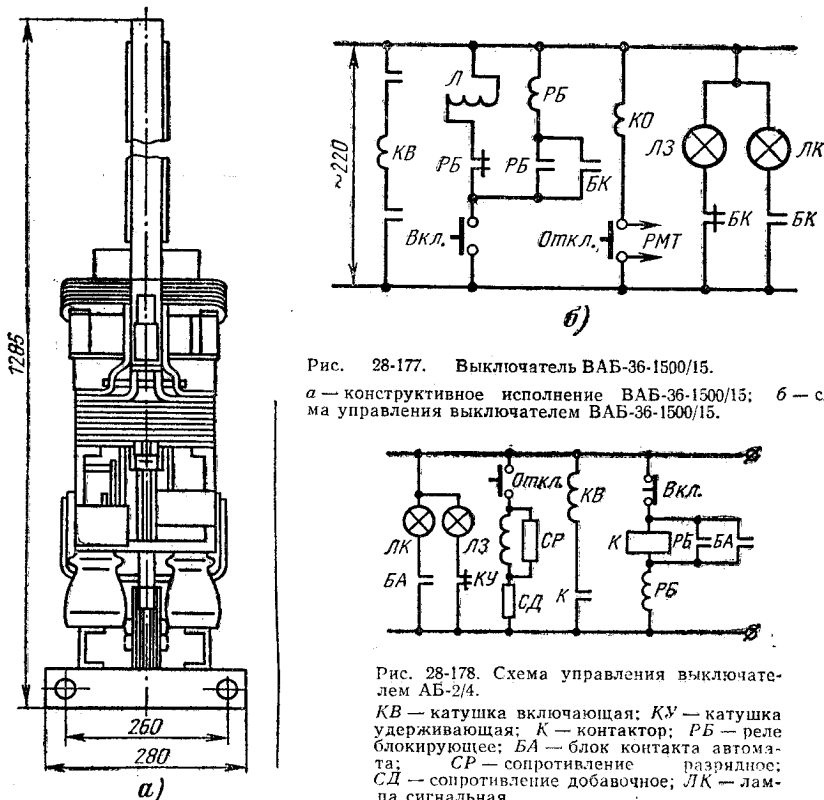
Выключатель ВАБ-36-1500/15.
